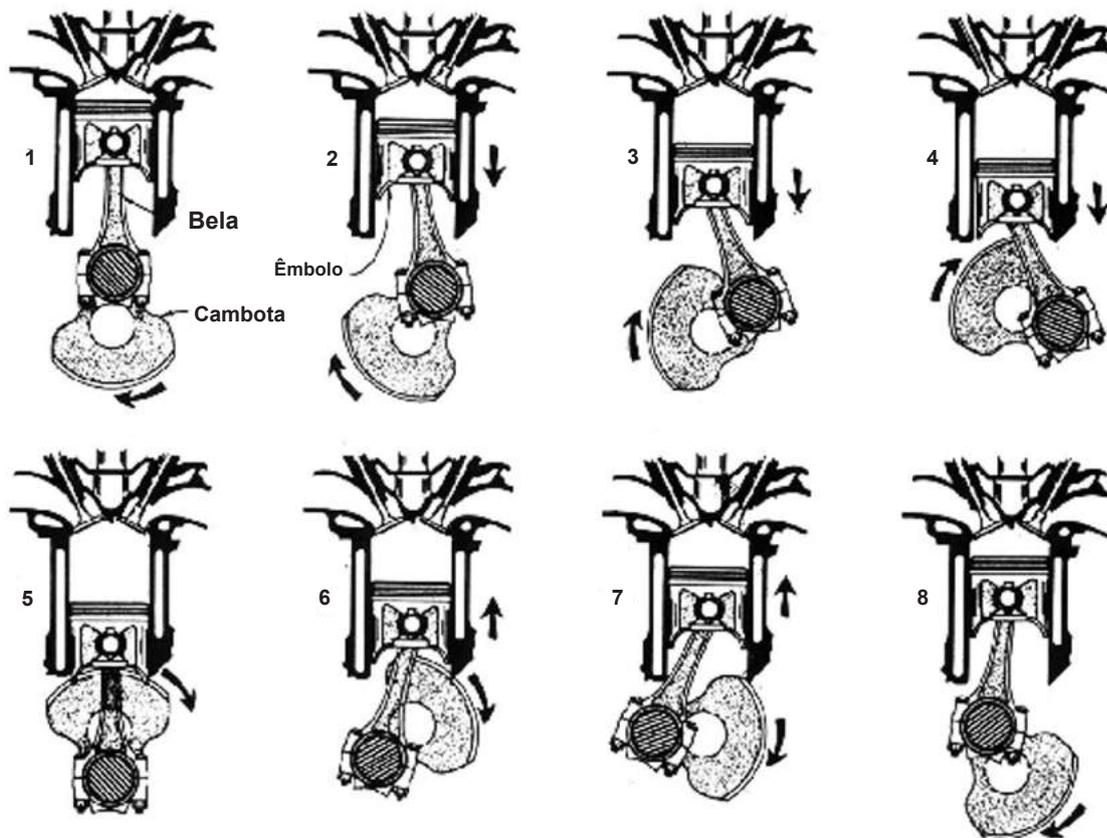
Transformação de movimento linear e alternativo de um êmbolo em movimento rotativo de uma cambota.
